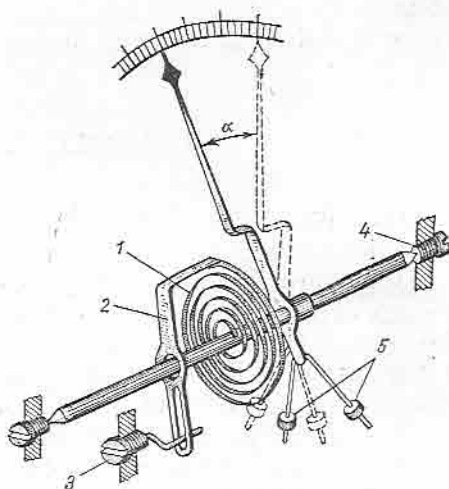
Echipaj mobil sprijinit în lagăre:
